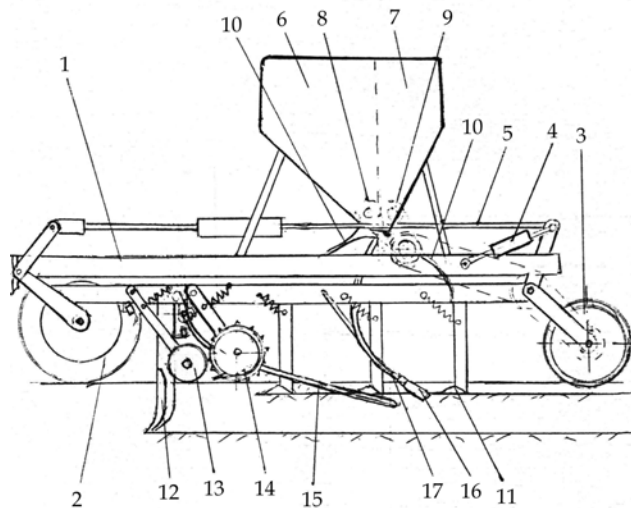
Почвообрабатывающе-посевной агрегат [6]: 1 – рама; 2 – самоустанавливающееся переднее колесо; 3 – опорно-прикатывающие катки; 4 – гидроцилиндр; 5 – рычажный механизм; 6 – бункер для семян; 7 – бункер для туков; 8 – зерновые высевальные аппараты; 9 – туковые высевальные аппараты; 10 – тукосемяпроводы; 11 – лаповые сошники; 12 – щелерезы; 13 – конусные катки; 14 – соломонаправитель; 15 – соломозаталкиватель; 16 – наконечник; 17 – тукпровод
